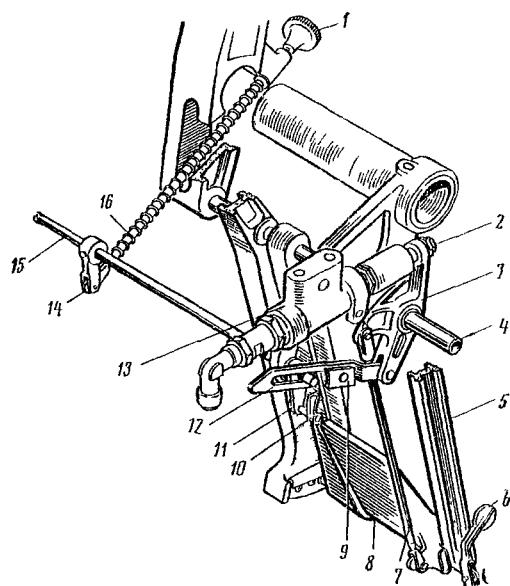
Механизм управления тормозным клапаном и стояночным торможением
